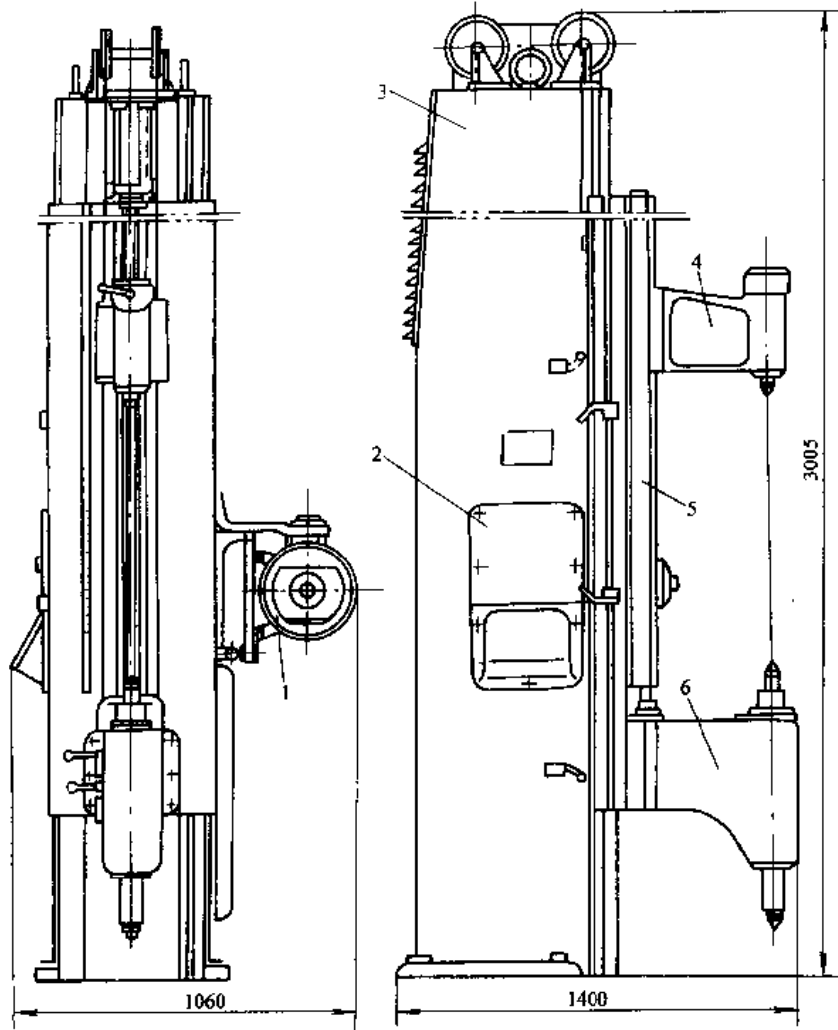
GC-1205 型轴及齿轮通用淬火机床简图
